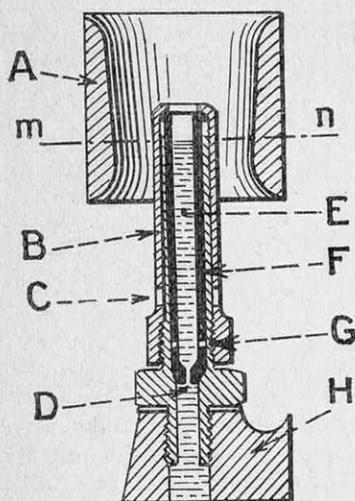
COUPE DU GICLEUR NOYÉ « SOLEX »
